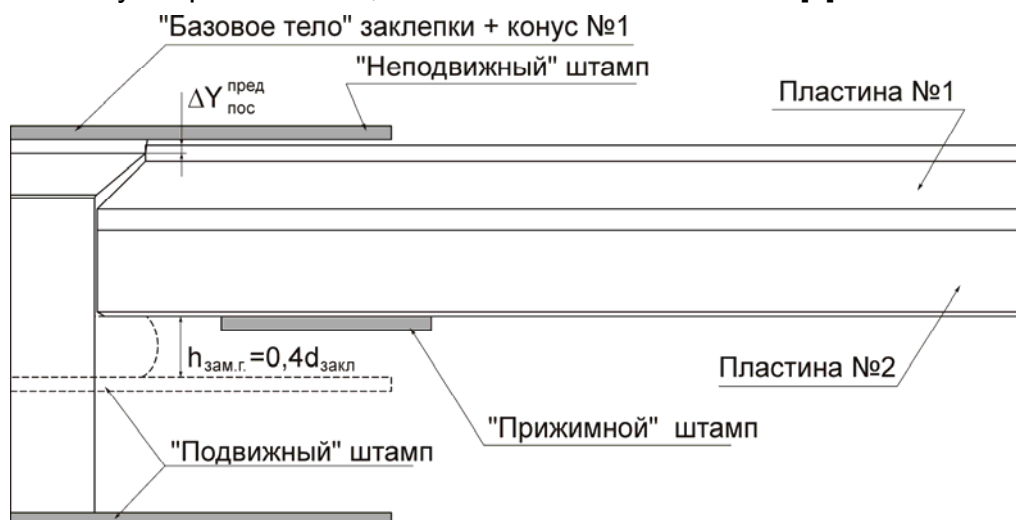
Схема формирования замыкающей головки разрабатываемой потайной заклепки
